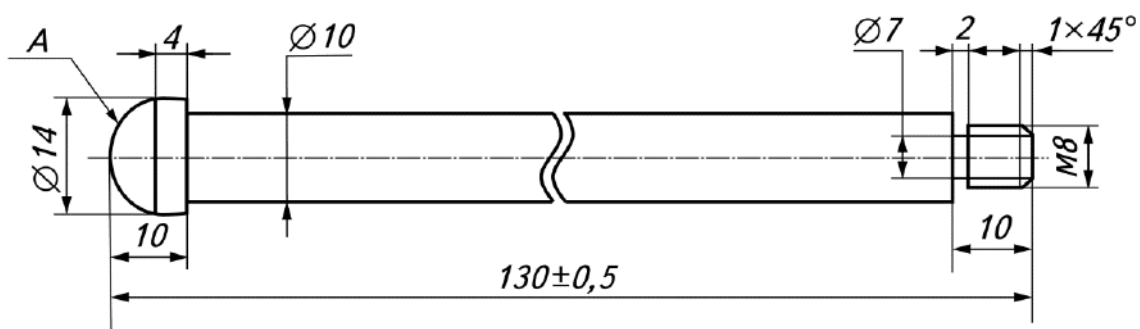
Рукоятка для винтового зажима столярного верстака
